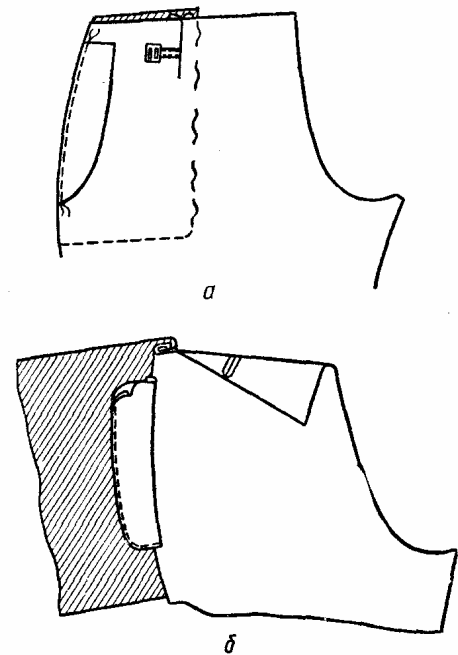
Обробка кишень у бокових швах з боку задньої половинки штанів.
